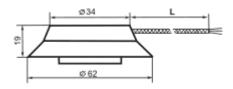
Внешний вид и габаритные размеры термопреобразователя.
